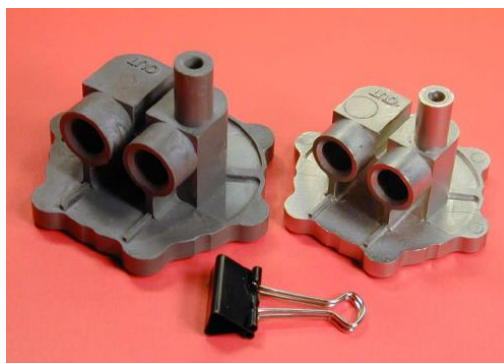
Pieza en marrón (izquierda) y pieza sinterizada (derecha) [40]
